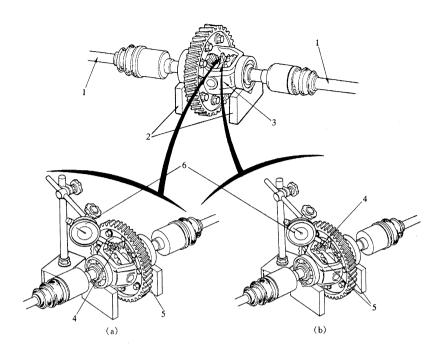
差速器行星齿轮与半轴齿轮啮合间隙的检测 1. 传动轴 2.V形铁架 3. 差速器总成 4. 行星齿轮 5. 半轴齿轮 6. 百分表
